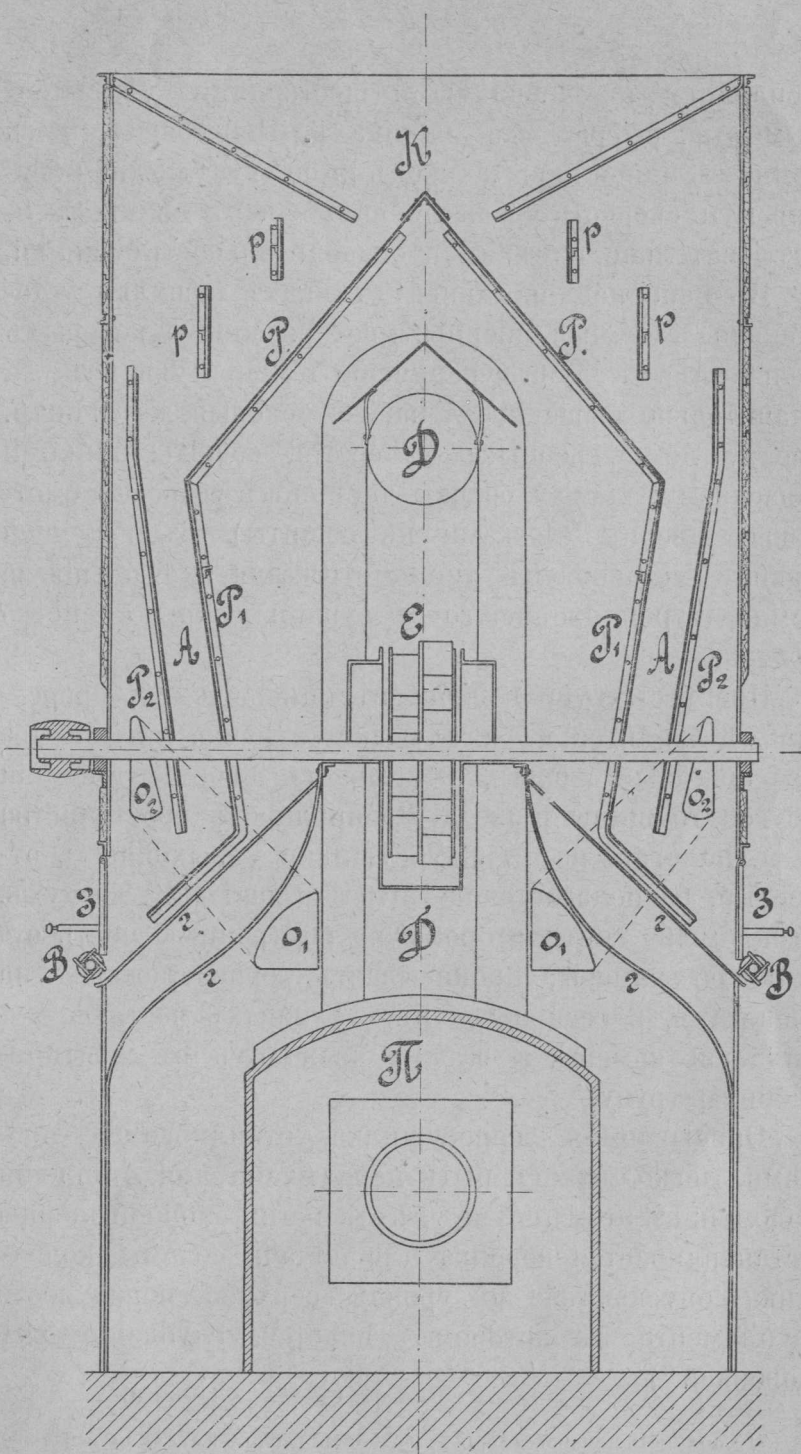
Вертикальный поперечный разрез механической зерносушилки Аккермана.
